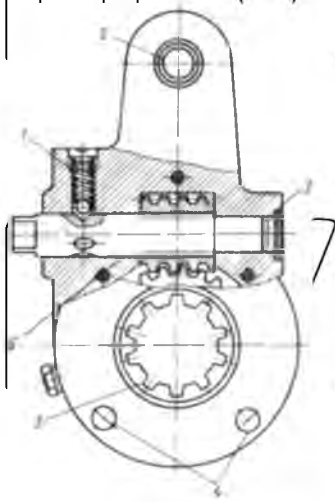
Регулювальний важіль в зборі 120-3501136
